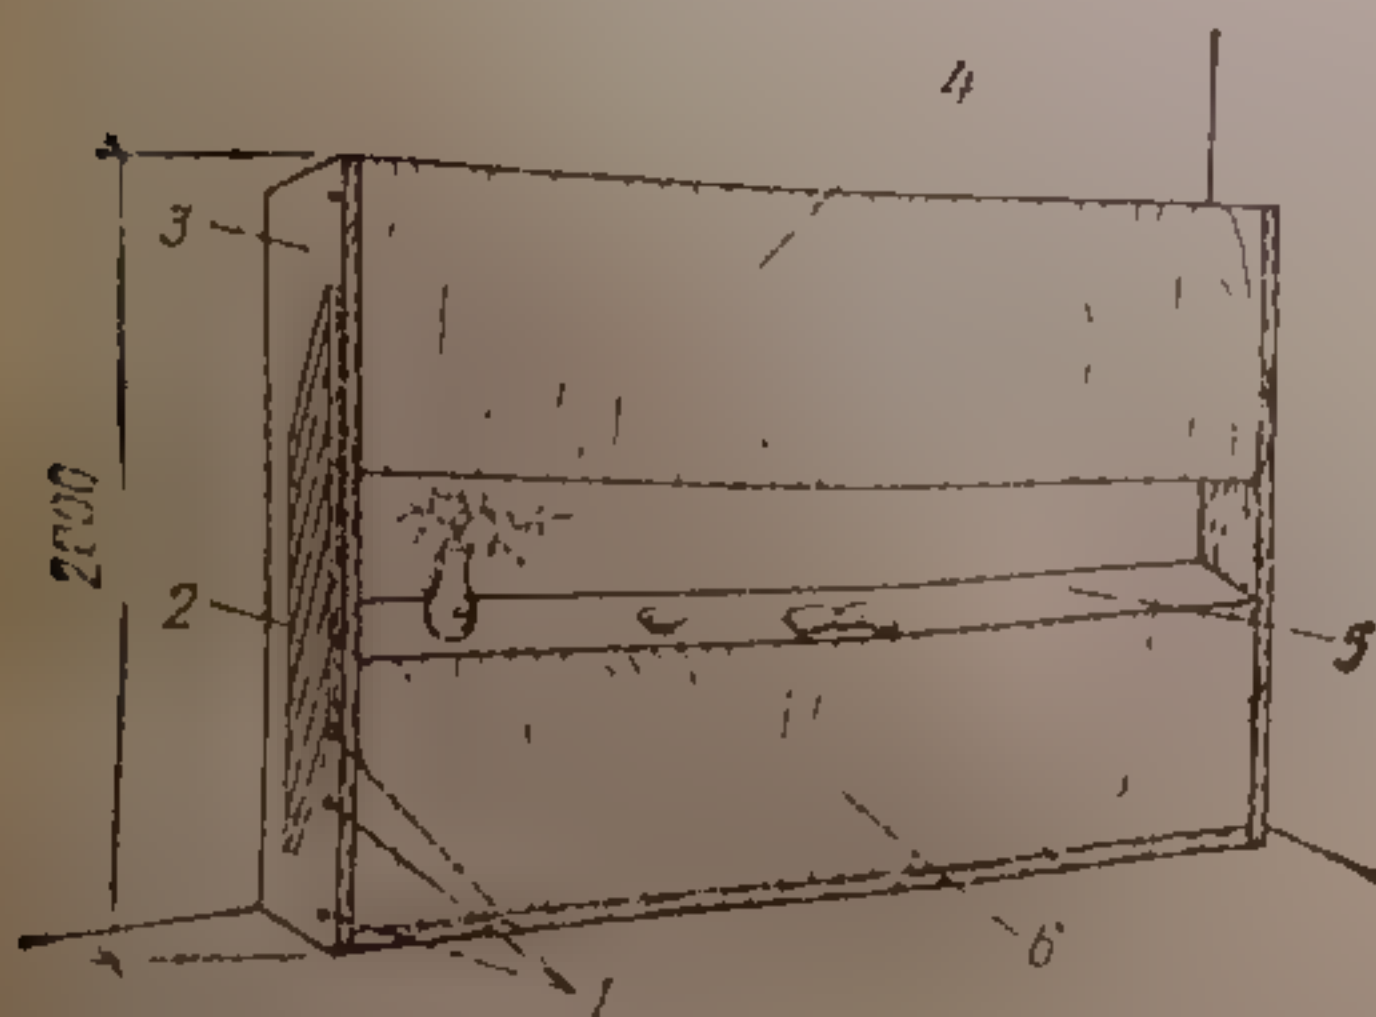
Общий вид мобильной, трансформирующейся двухъярусной детской кровати: 1 — ось-шарниры; 2 — складная лестница; 3 — стойка короба кровати; 4 — верхняя крышка; 5 — откидная доска; 6 — нижняя крышка
